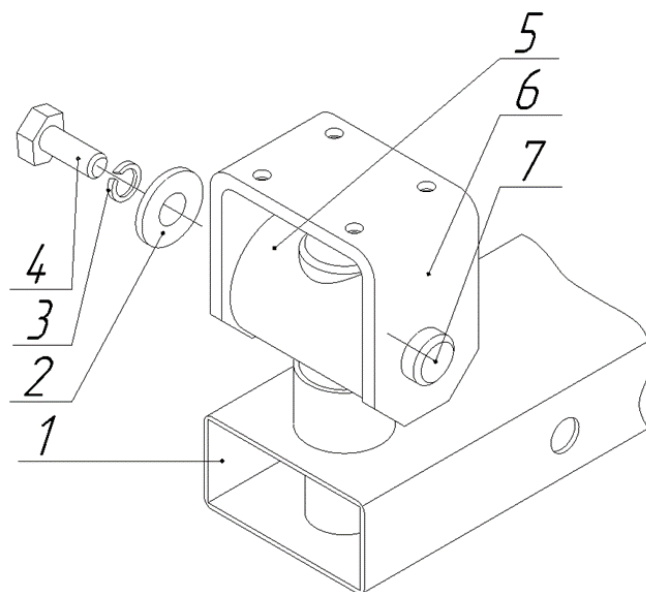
Конструкция устройства крепления блоков извещателя при помощи поворотного устройства на кронштейне КМ1.
